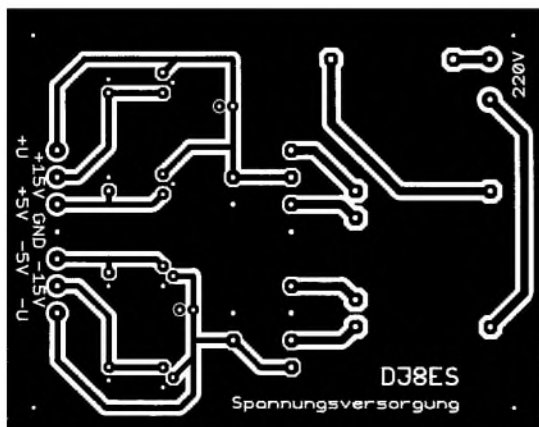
Platinenlayout zur Schaltung gemäß Bild 10
